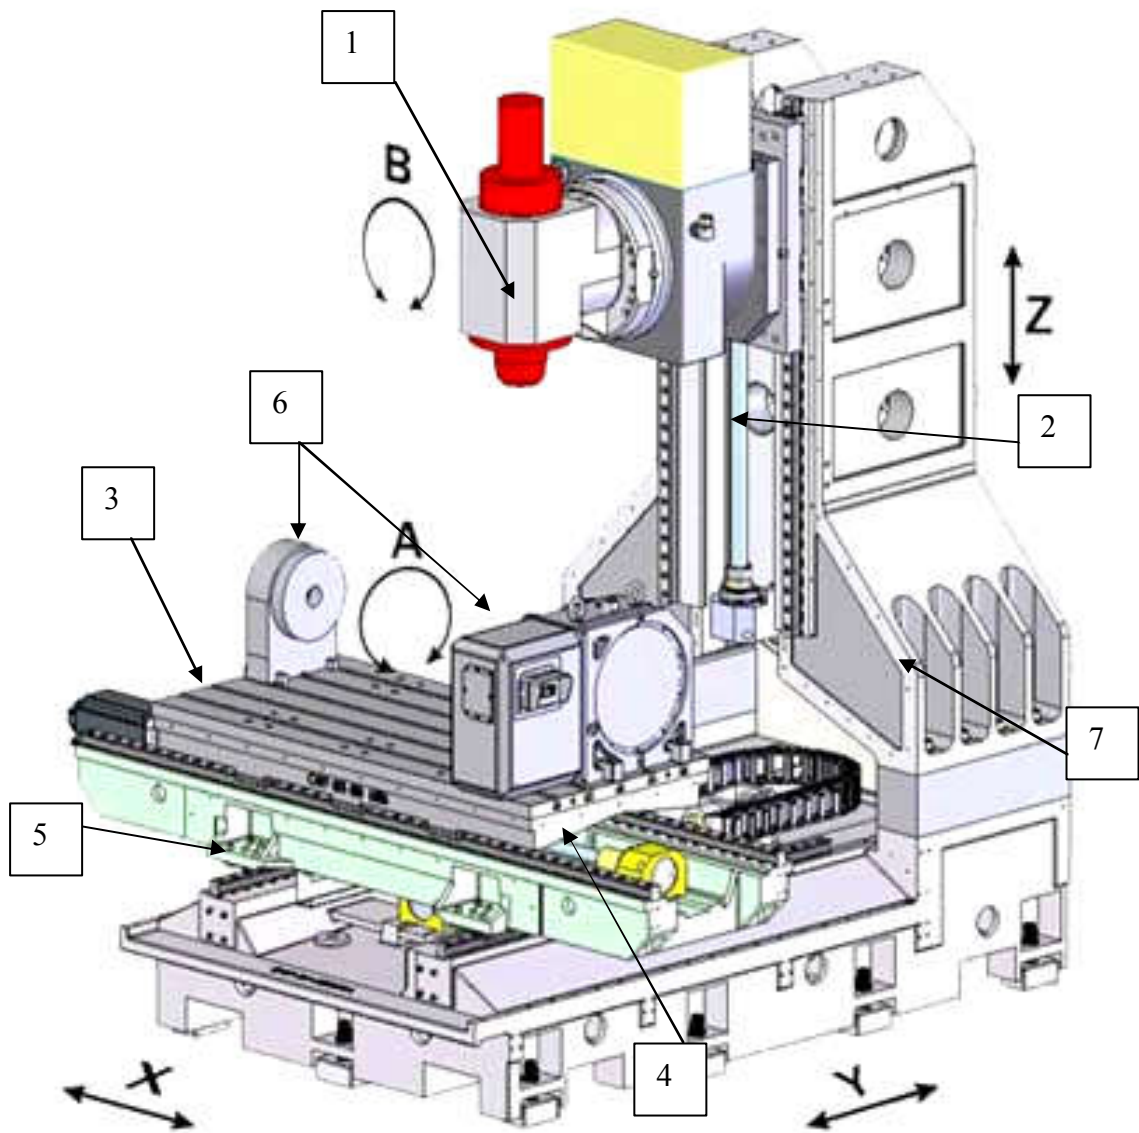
Схема вертикально-фрезерного пятикоординатного обрабатывающего центра
